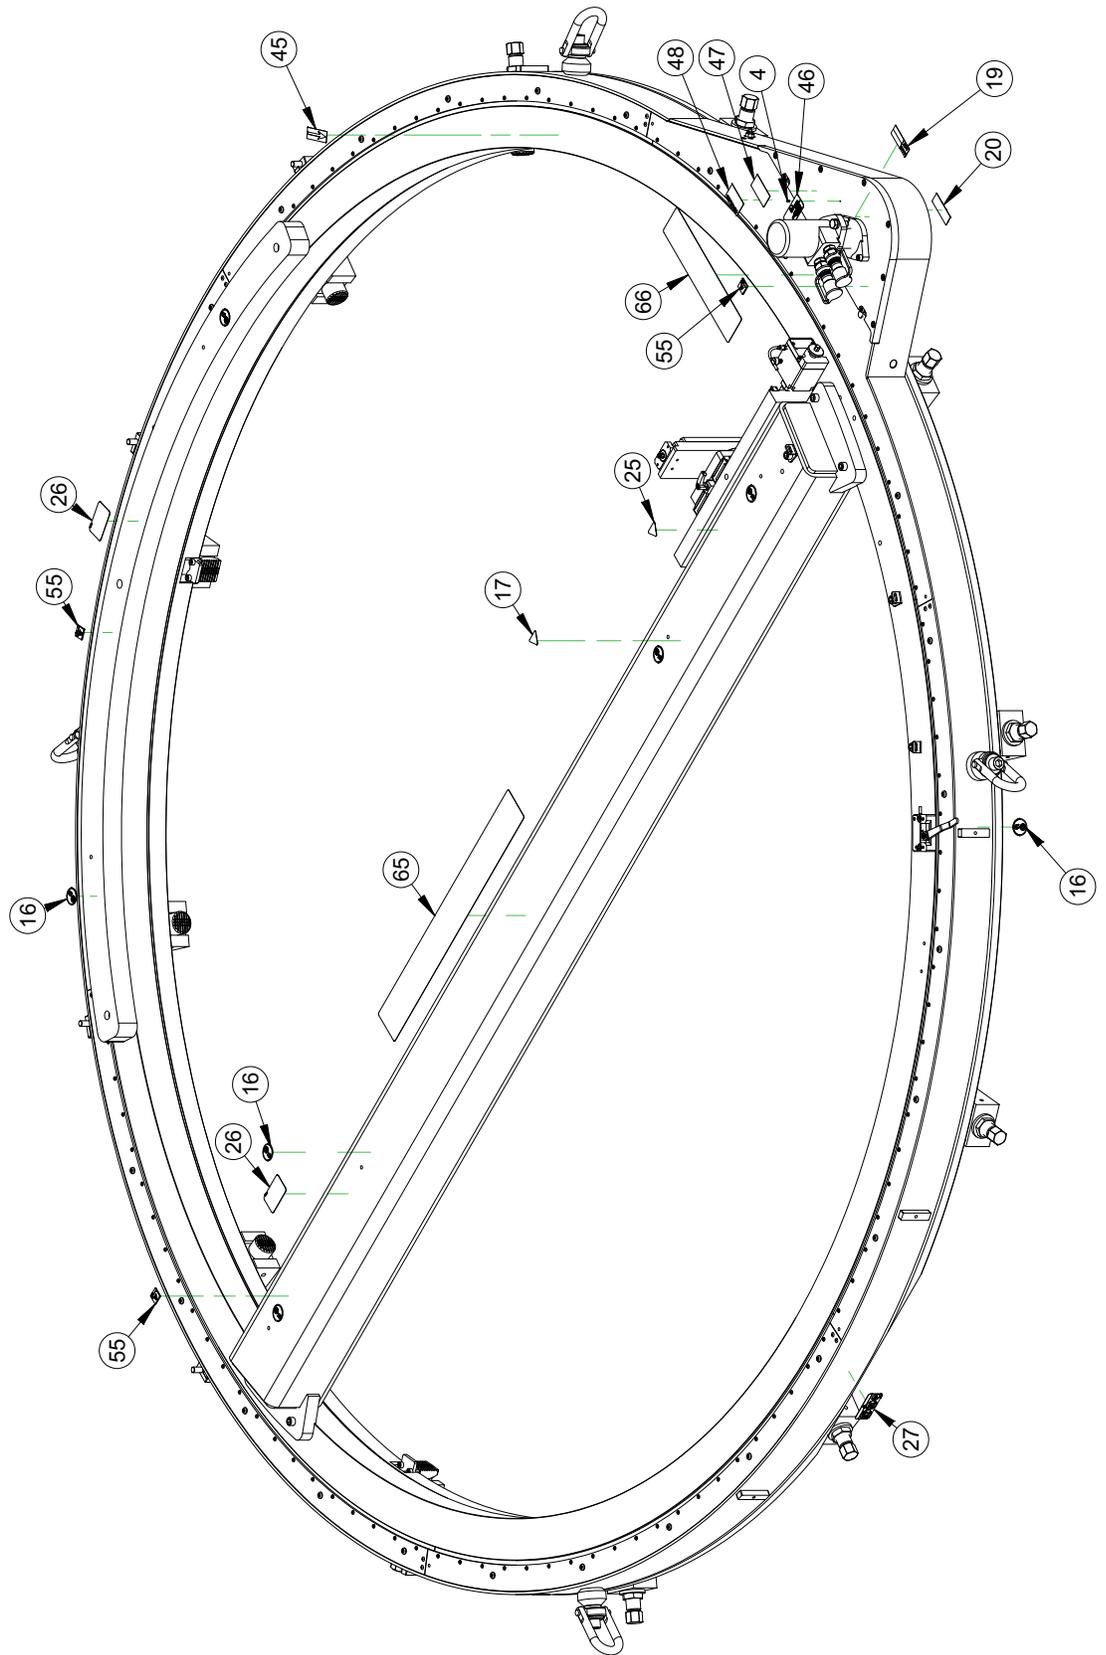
ODF120 SPEED FACER EMBLEMES DES ÉTIQUETTES (RÉF. 89210)
